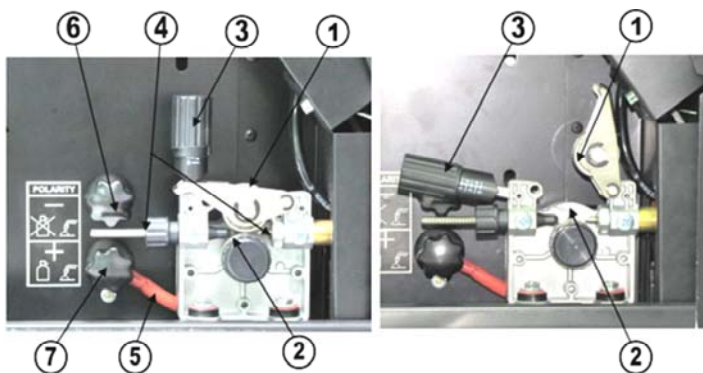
Механизм подачи сварочной проволоки:
